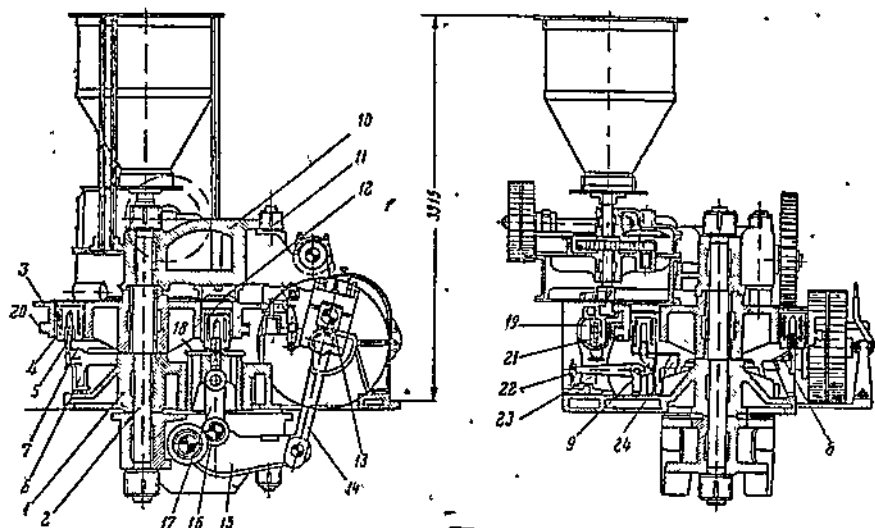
План и разрез пресса с поворотным столом системы Дорстен: 1 — рама пресса; 2 — колонка-ось поворотного стола; 3 — поворотный стол; 4 — штемпель; 5 — ролики штемпелей; 6 — сегментные стойки; 7 — стальные шины; 8, 9 — скосы шин; 10 — обойма; 11 — болты крепления обоймы к раме; 12 — плита, воспринимающая давление в прессе; 13 — коленчатый вал; 14 — насаженный на вал шатун; 15 — рычаг; 16 — ось подвески рычага; 17 — толкач давления на штемпель; 18 — штамп того же давления; 19 — зубчатая рейка; 20 — кольцо, опоясывающее стол; 21 — зубчатый сегмент; 22 — шпиндель; 23 — рычаг регулирования наполнения; 24 — передвигная часть шинного пути
